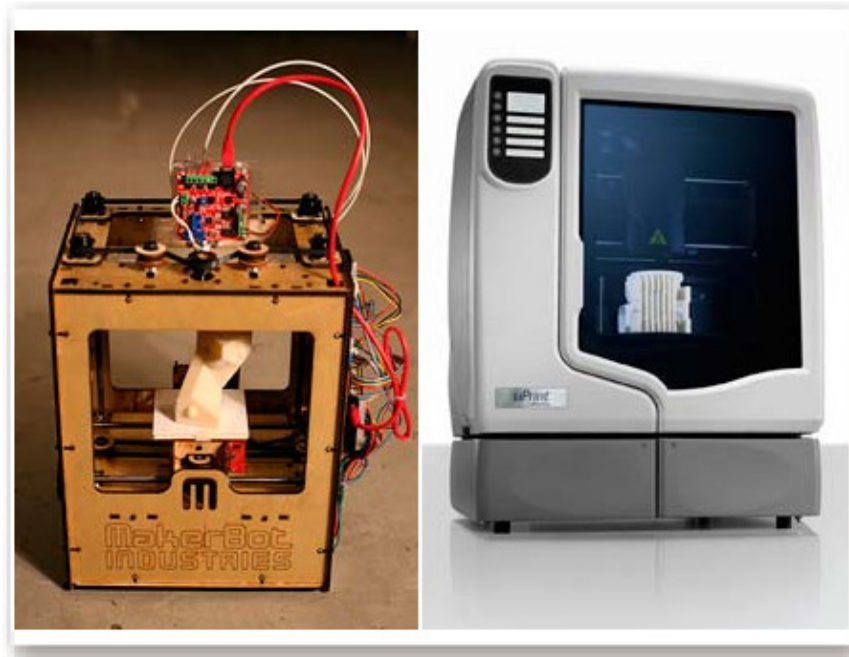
MakerBot Cupcake CNC (esquerda) e Stratasys Dimension uPrint (direita).
